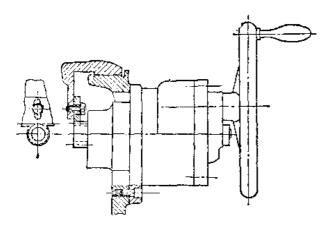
利用长孔来调节齿条与齿轮的啮合位置
